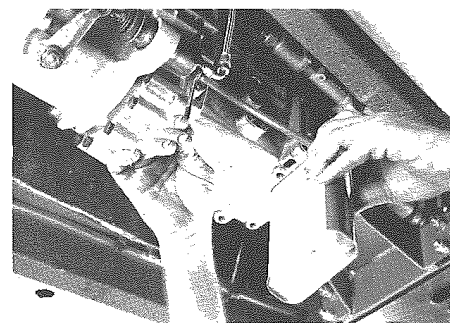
Fissaggio del tubo flessibile alla vite di spurgo
